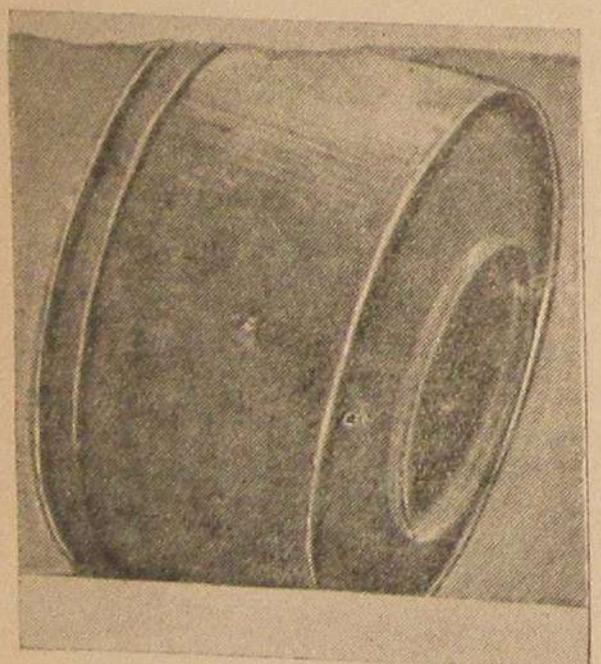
Верхний наружный кожух газогенератора ЛС-1-3, komplektino изготовлением в Монетном мхлесопункте.
